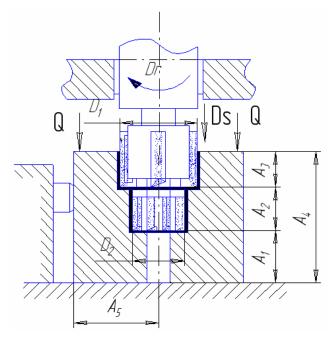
Базирование заготовки для обработки ступенчатого отверстия
